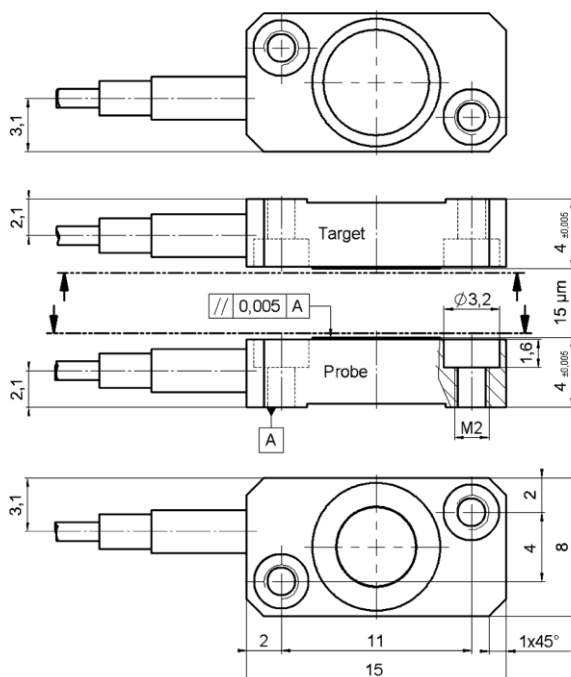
Габаритный чертёж датчика D-015.00. Размеры указаны в мм.
